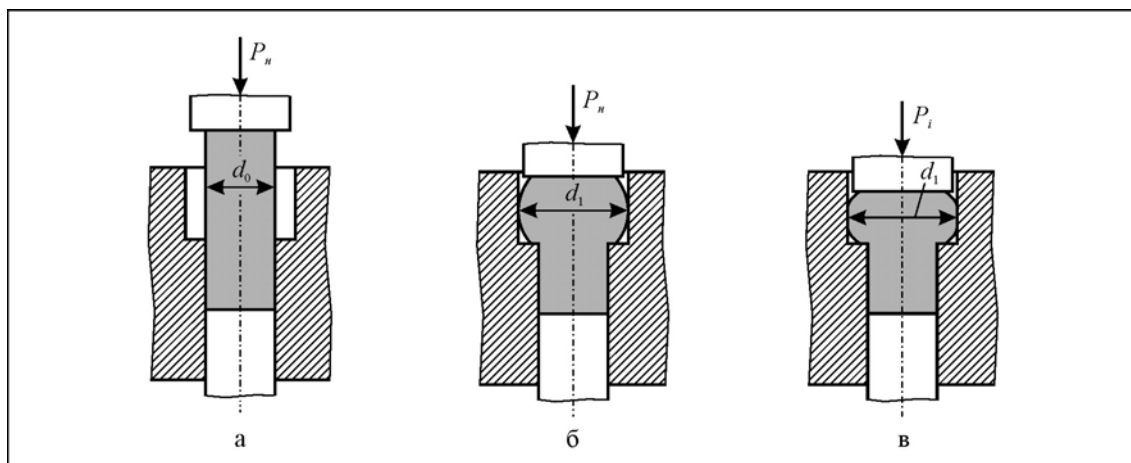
Схема закритого висаджування суцільної заготовки: а – початкова фаза; б – момент зіткнення частини заготовки з бічною стінкою штампа; в – проміжний момент висаджування
